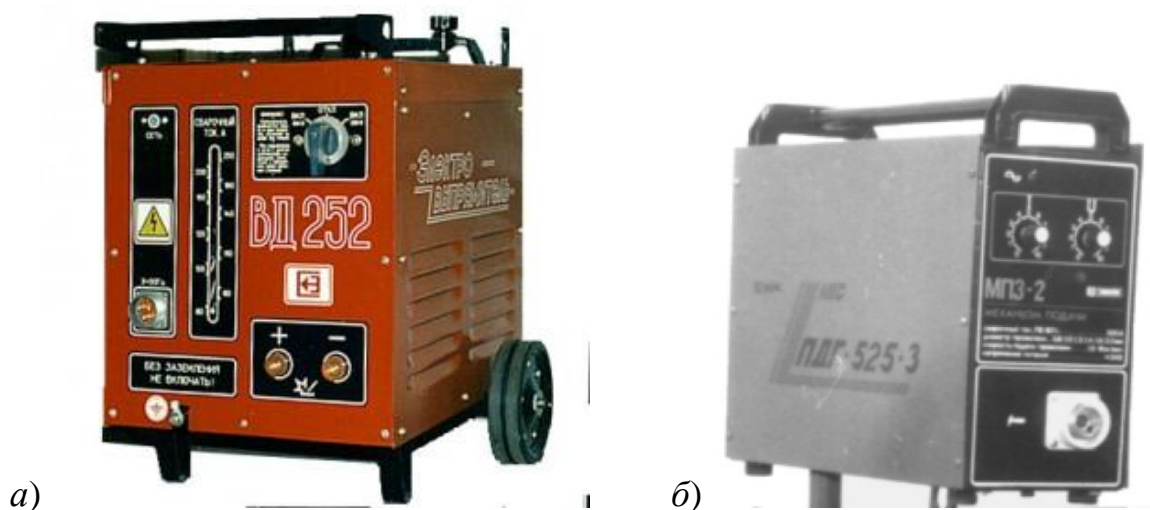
Оборудование для заварки разделанной трещины: сварочный выпрямитель ВД-252 (а) и сварочный полуавтомат ПДГ-525 (б)
